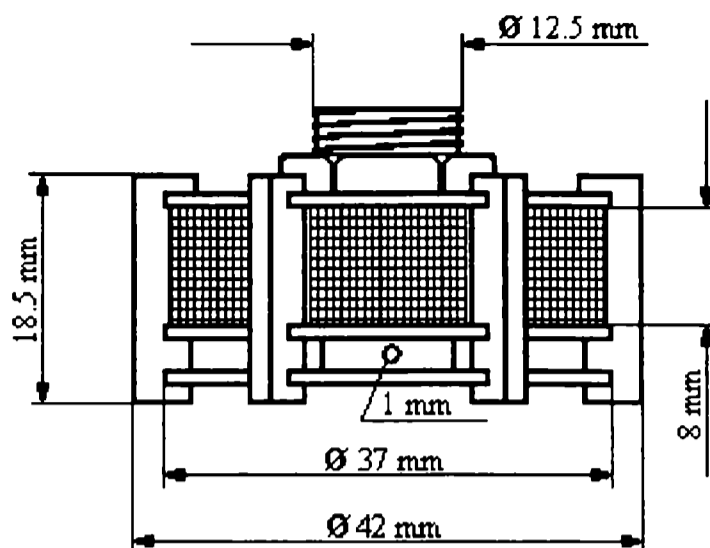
Vista frontal del dispositivo de canastas rotatorias, dimensiones principales.
